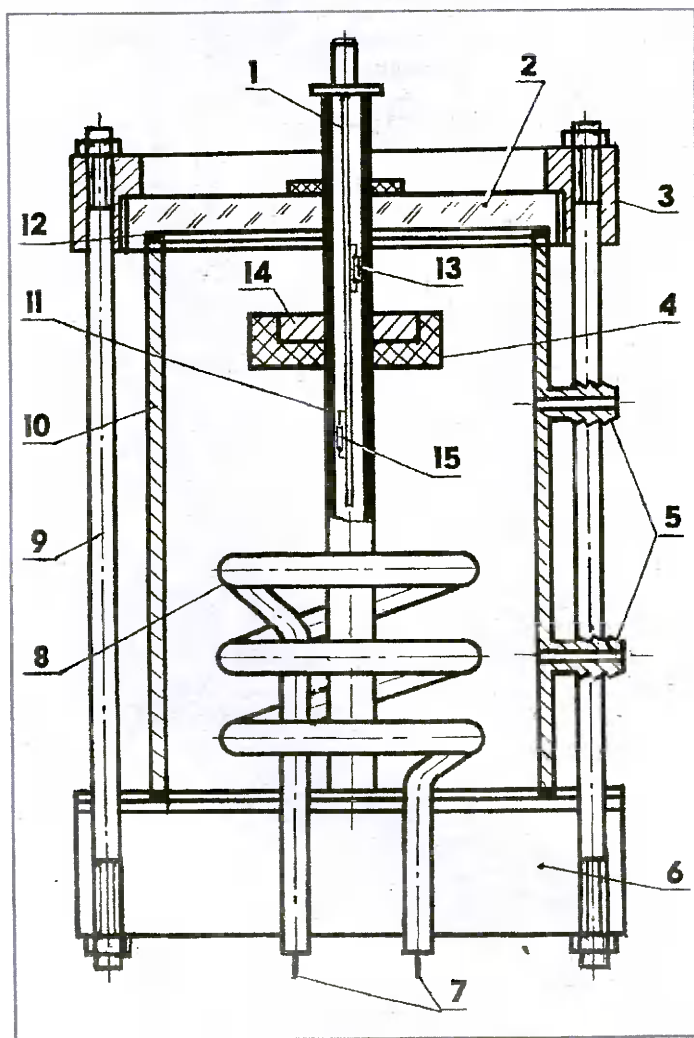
Устройство котла. Цифрами обозначены: 1 — плата датчиков; 2 — окно; 3 — фланец; 4 — поплавок; 5 — штуцер; 6 — щиток; 7 — контакты; 8 — ТЭН; 9 — шпилька М6х250; 10 — корпус; 11 — гнездо датчиков; 12 — прокладка; 13 — геркон с нормально замкнутыми контактами; 14 — кольцевой постоянный магнит; 15 — терморезистор R4.
